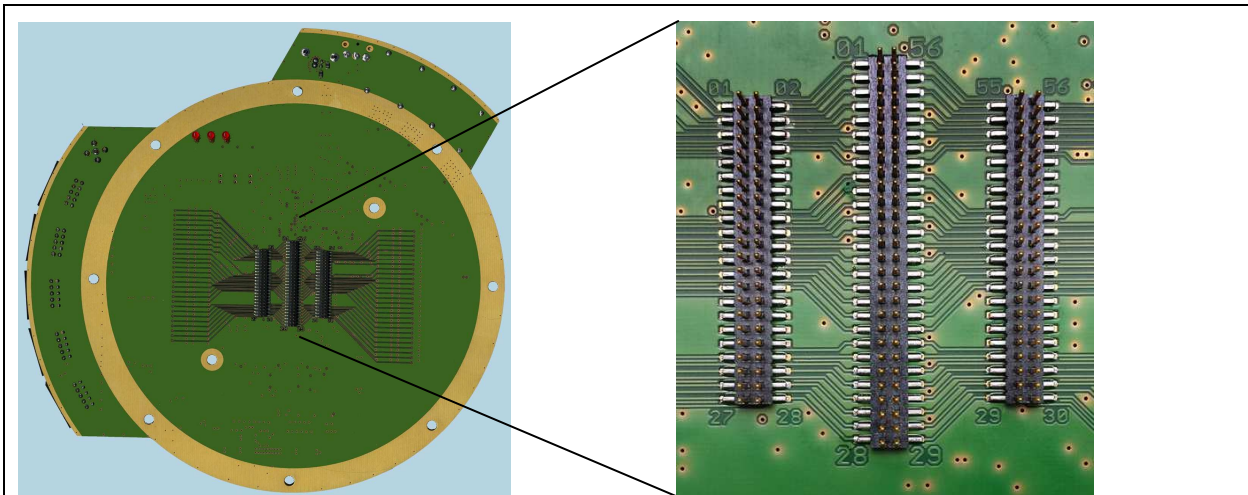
Stecker für die Testleiterkarte auf der Top-Seite des Connection Boards CB 0708
